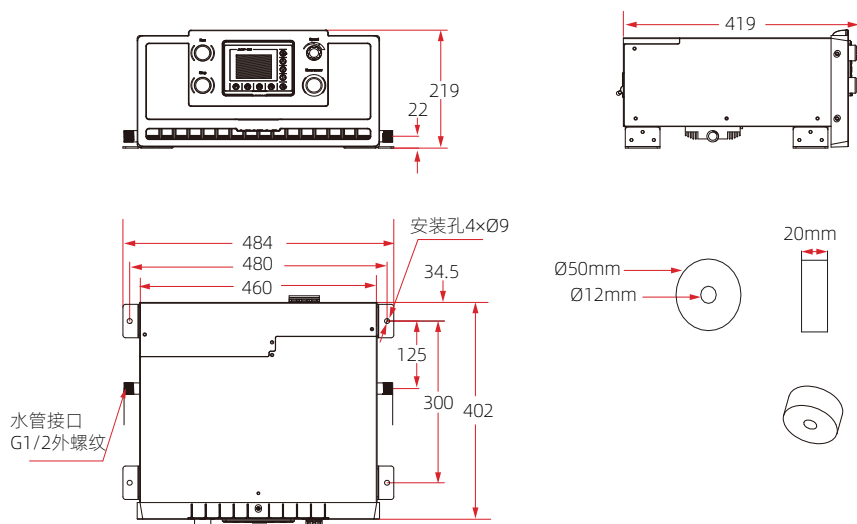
（标准机型 - 一体液冷 - 侧出冷却管）外型尺寸安装尺寸及减震垫示意图 (AWD100-4T0501~AWD100-4T1804) (单位: mm)
